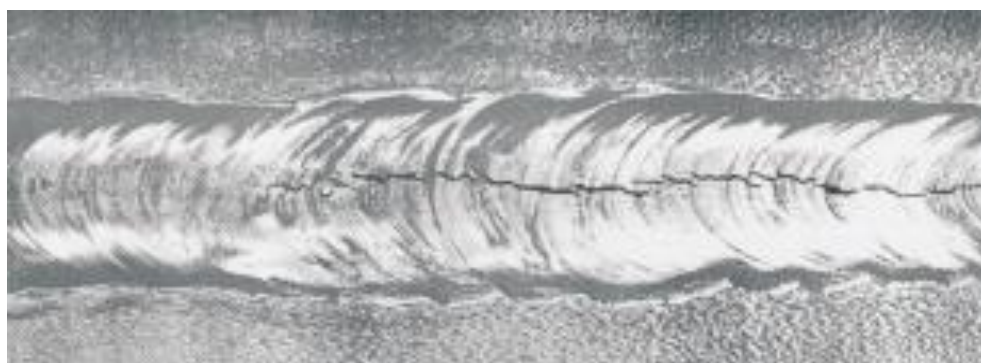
Горячие трещины при сварке сплава АМгбМ
